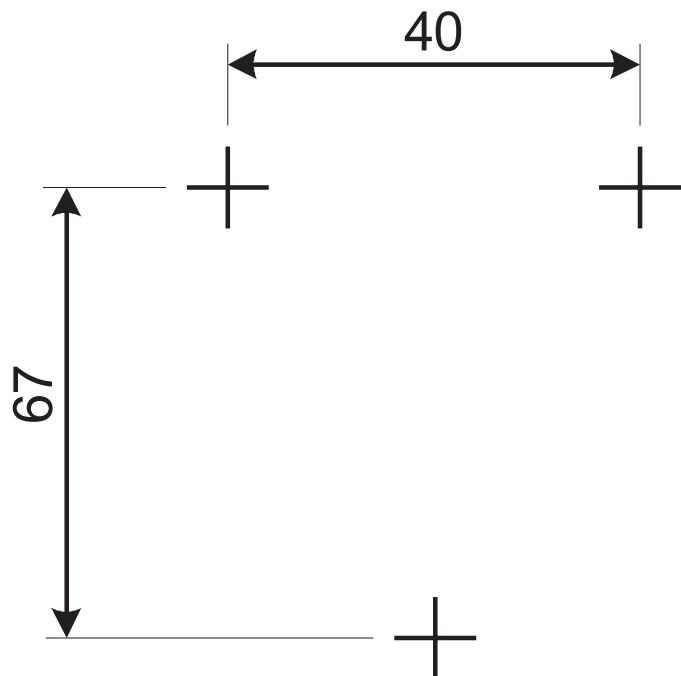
Эскиз посадочных мест для крепления корпуса прибора
